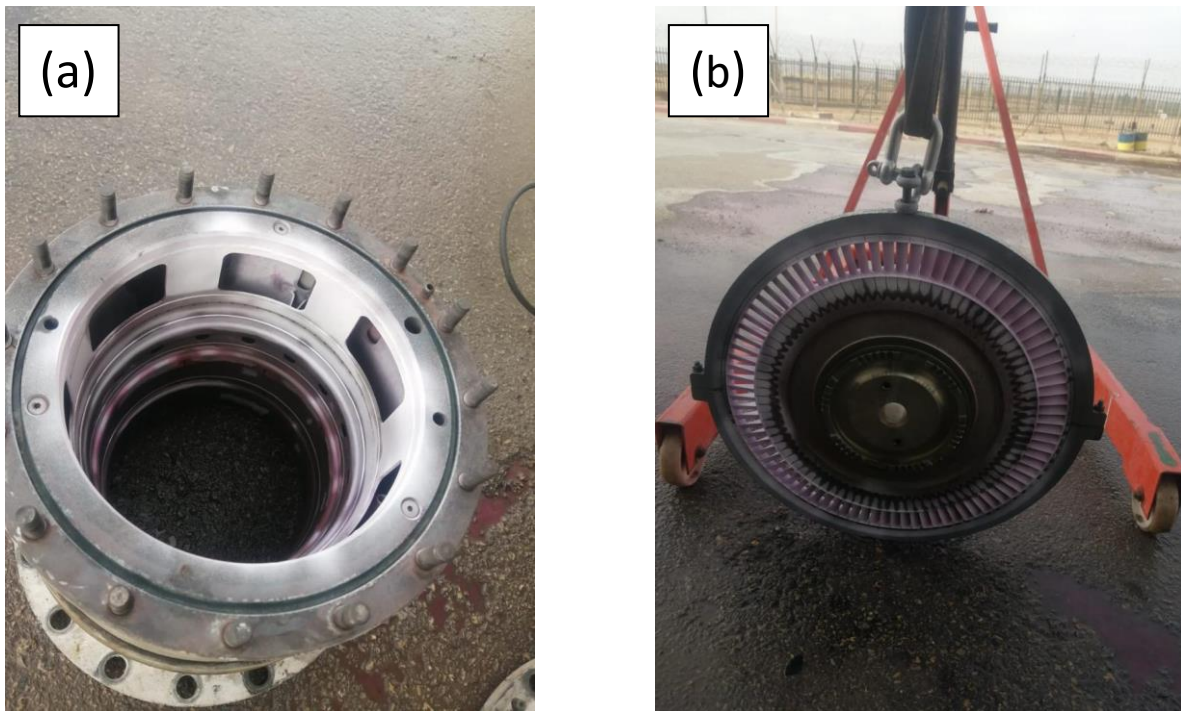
(a) chambre de combustion de LM5000, (b) la roue de LM5000
